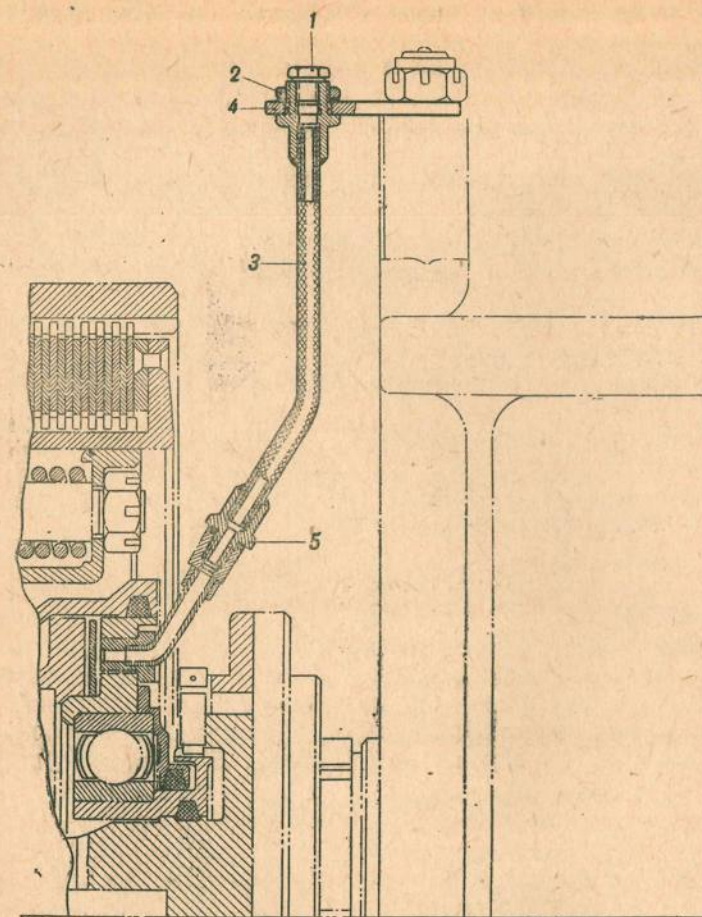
Установка шланга для смазки подшипника поводковой коробки бортового фрикциона
